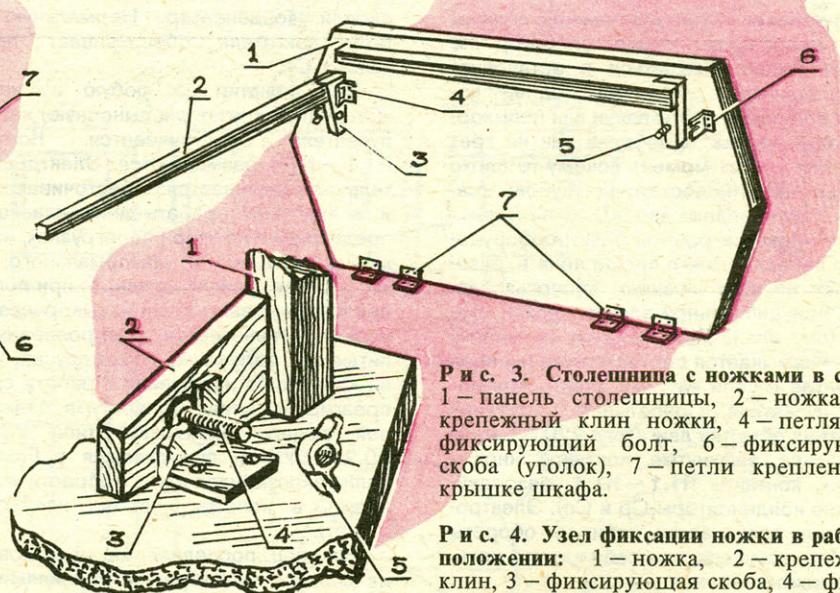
Столешница с ножками в сборе: 1 — панель столешницы, 2 — ножка, 3 — крепежный клин ножки, 4 — петля, 5 — фиксирующий болт, 6 — фиксирующая скоба (уголок), 7 — петли крепления к крышке шкафа.
